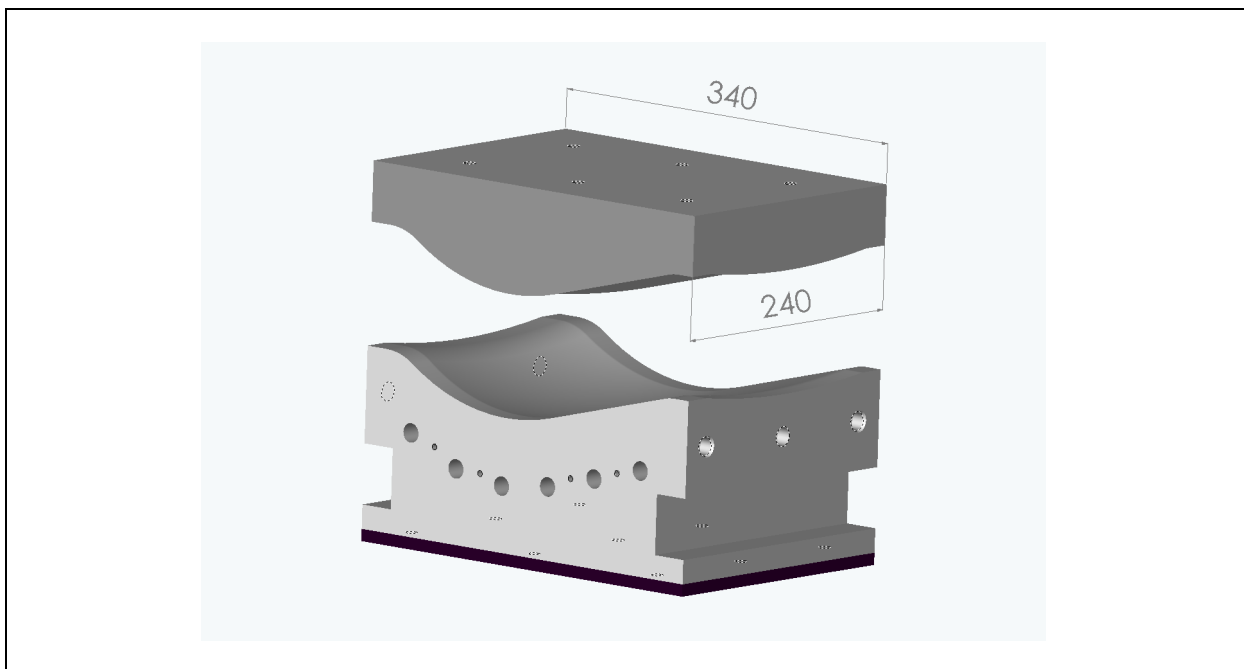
CAD-Zeichnung des eingesetzten Werkzeugs
